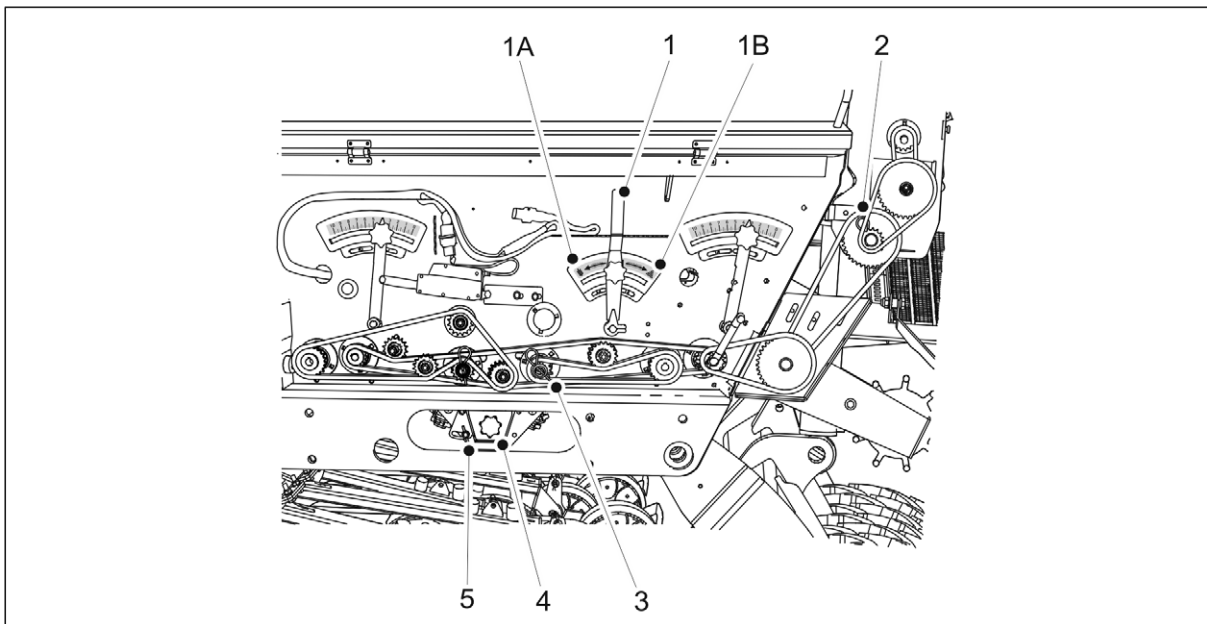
122. Kalibreringsprov med justering av gödselmedlets målshastighet på en maskin med en dubbel växellåda.
